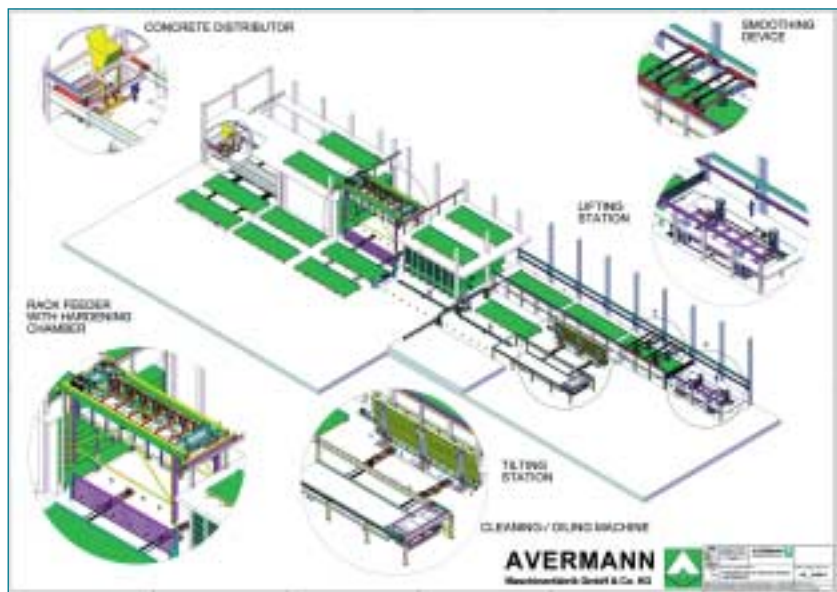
Fotos de la planta con ejemplos de la maquinaria.
